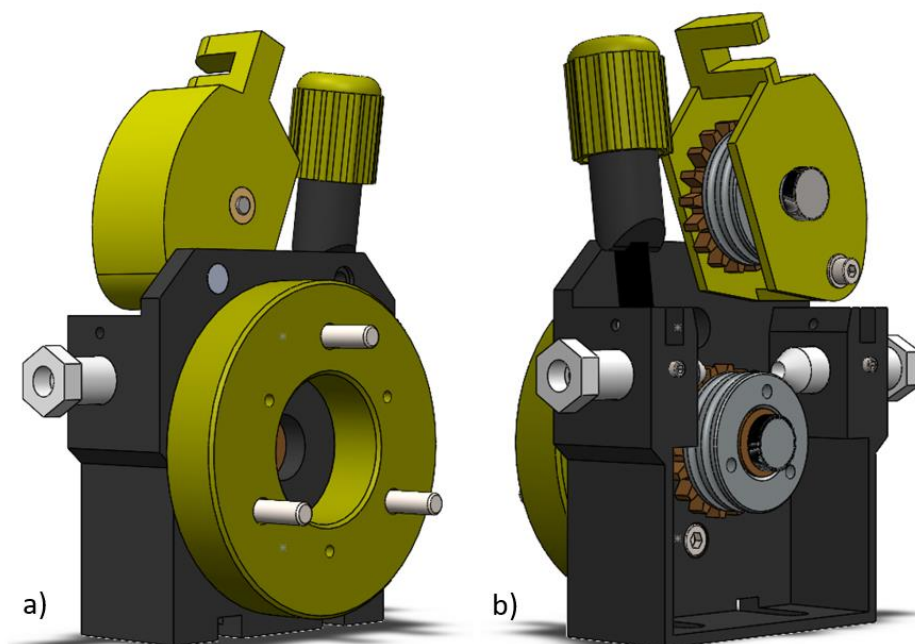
Primeiro protótipo do sistema de alimentação de fio de soldadura a) vista de trás, b) vista de frente
